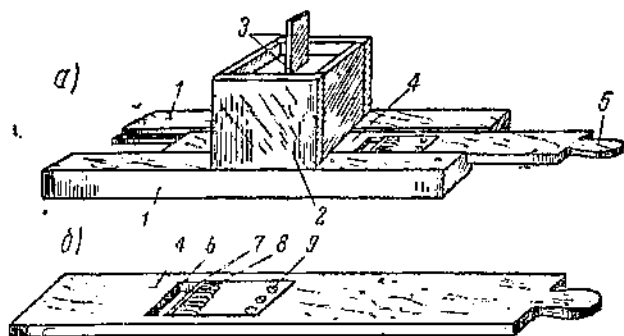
Ручная шинковка для корнеплодов: а) 1—станина с ползками; 2—загрузочный бункерок для корнеплодов; 3—прижим с рукояткой; 4—подвижная доска с ножом; 5—рукоятка подвижной доски б) 6—отверстие в доске под ножом; 7—нож для резки на кружки или пластинки; 8—поперечные ножи (гребенка) для резки пластинок на столбики (лапшу); 9—винты для крепления ножа
